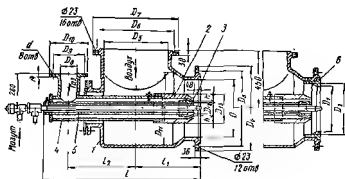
Газомазутные горелки для нагревательных печей завода «Серп и молот». 1 — корпус горелки; 2 — газовое сопло, 3 — форсунка высокого давления; 4 — газопроводящая труба, 5 — центральная труба, 6 — воздушная насадка
